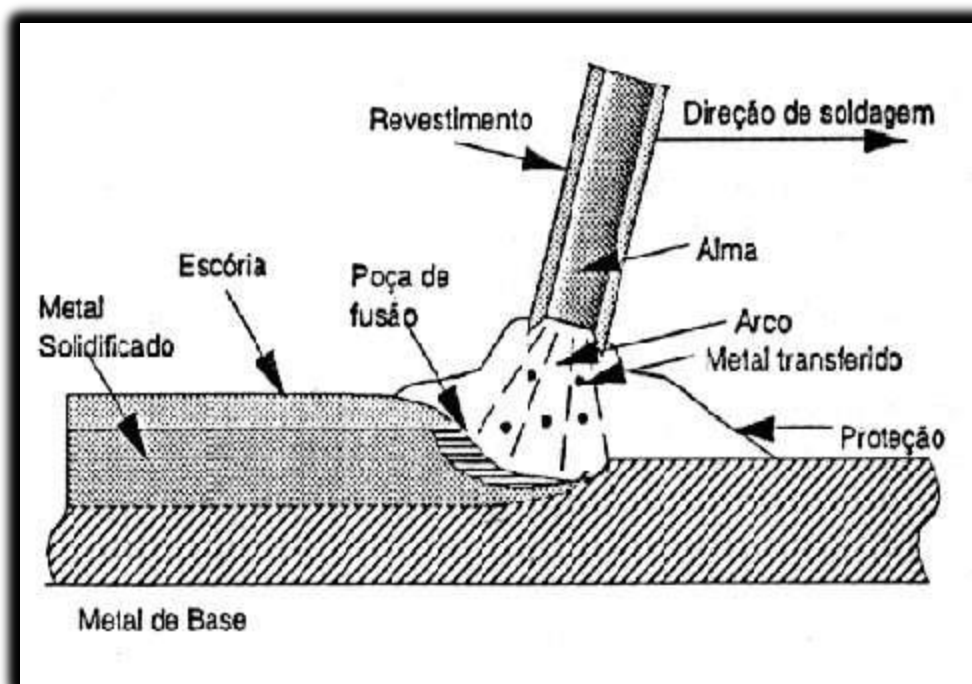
Soldagem com Eletrodo Revestido (Bracarense, 2014).
